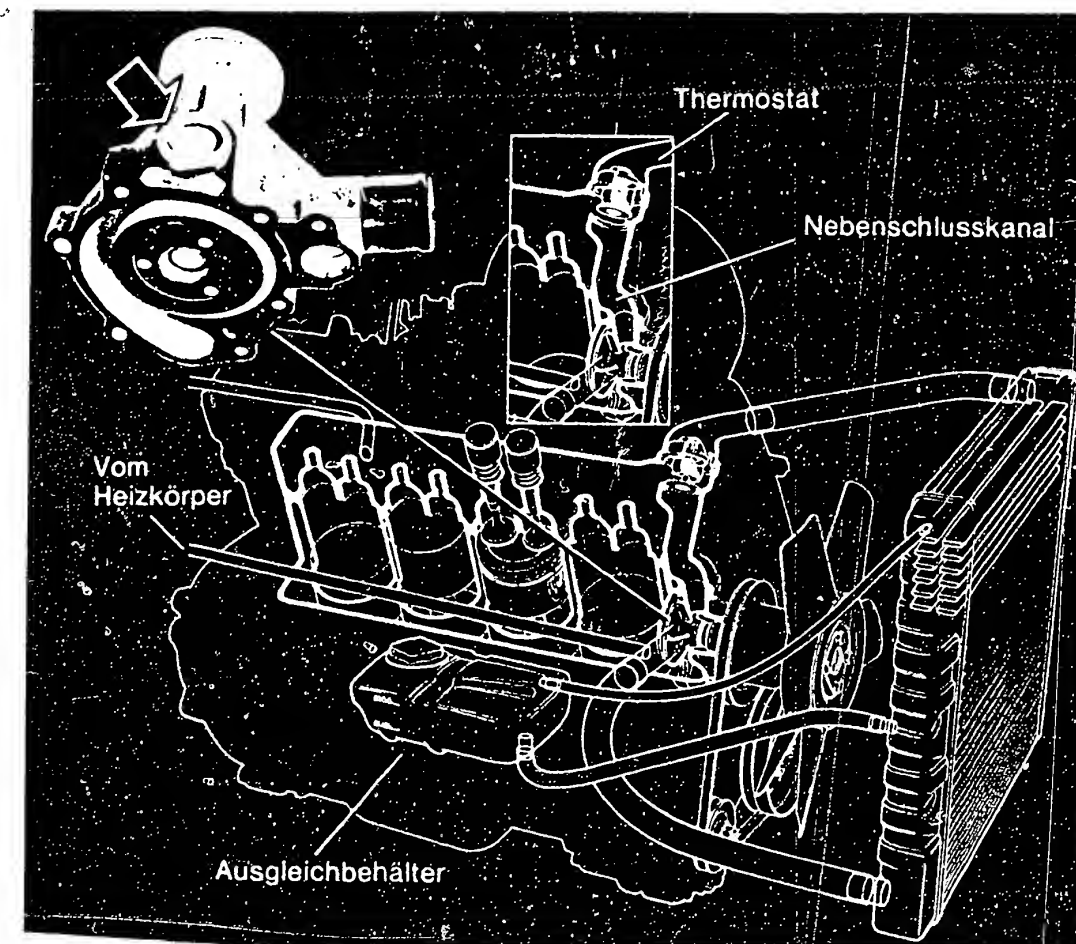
Kühlsystem mit Ausgleichsbehälter. Die Wasserpumpe ist gegen den Zylinderkopf hin mit einem O-Ring abgedichtet.
